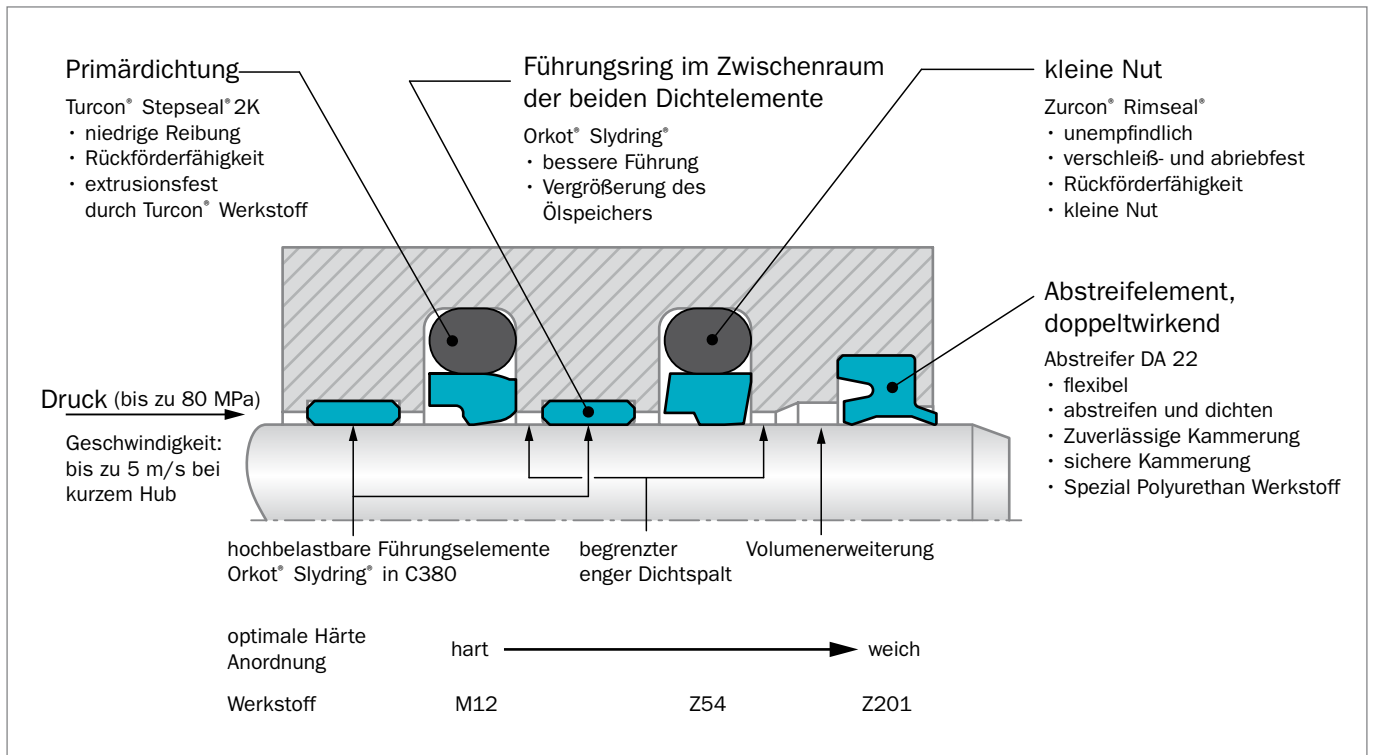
Beispiel für ein modular aufgebautes redundantes Dichtsystem
